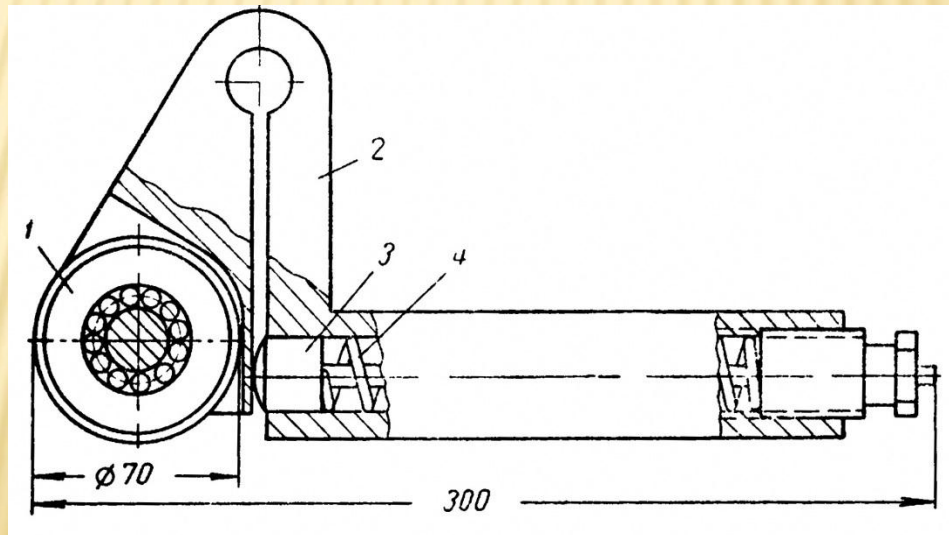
Універсальний однороліковий пристрій для обкочування зовнішніх поверхонь
